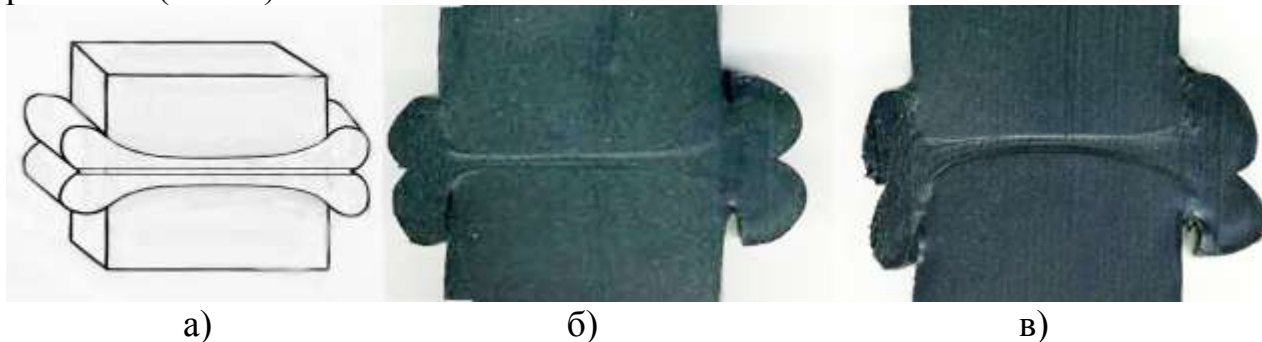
Перераспределение расплава при сварке труб с вертикальным расположением осей
